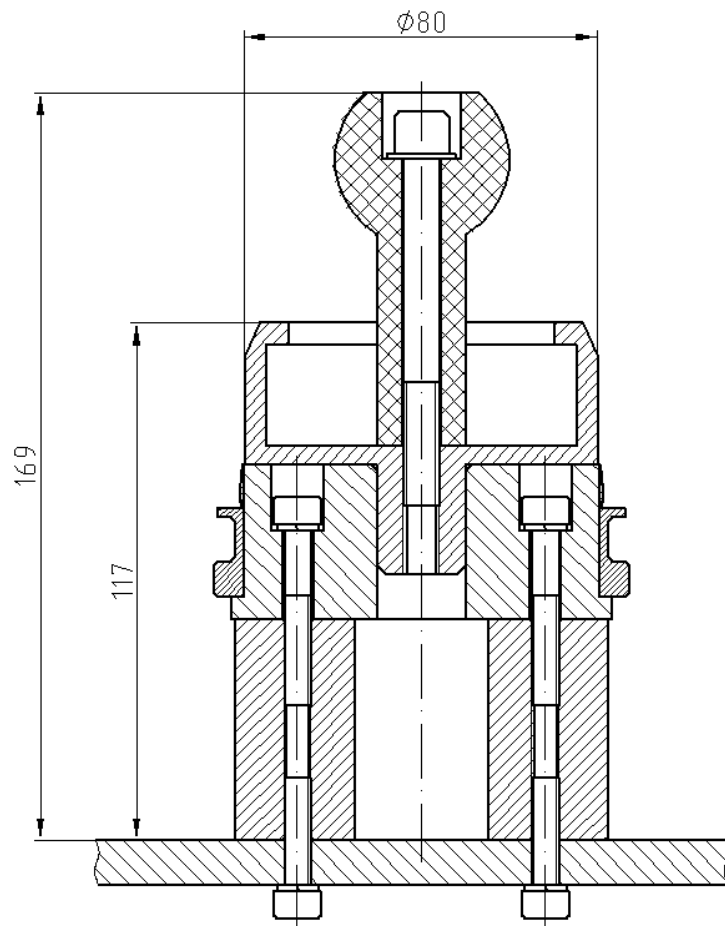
ЗМ 7820-4733 – Приспособление для установки сальникодержателя с сальником без пружины
